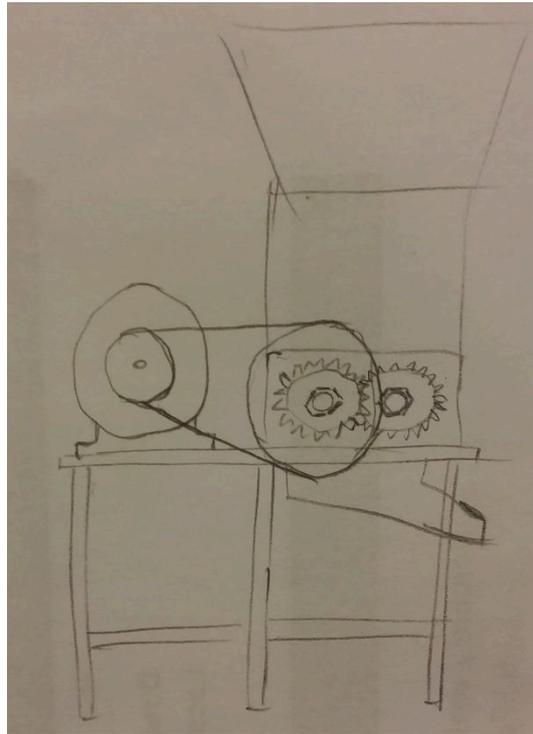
Vista de perfil de los elementos de la trituradora colocados en la mesa.
